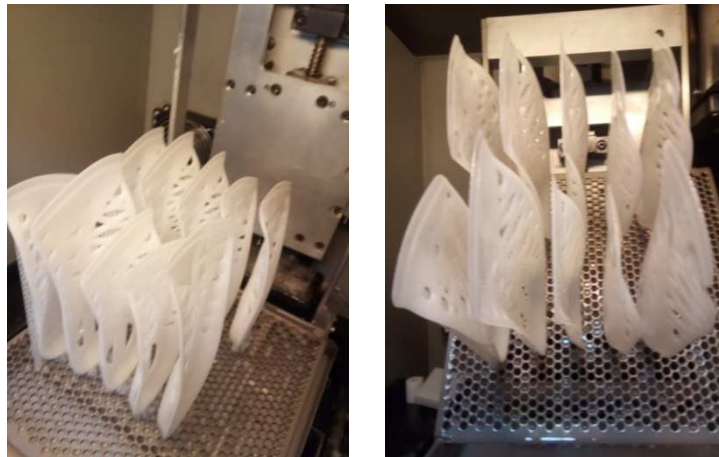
Soportes rígidos de las plantillas en la máquina de SLA tras acabar la fabricación
